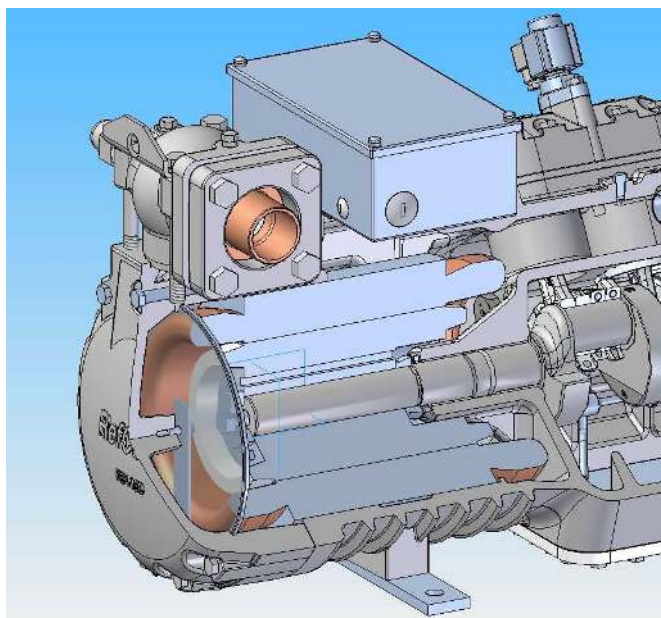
Положение всасывающего фильтра в моделях с 6 и 8 цилиндрами
